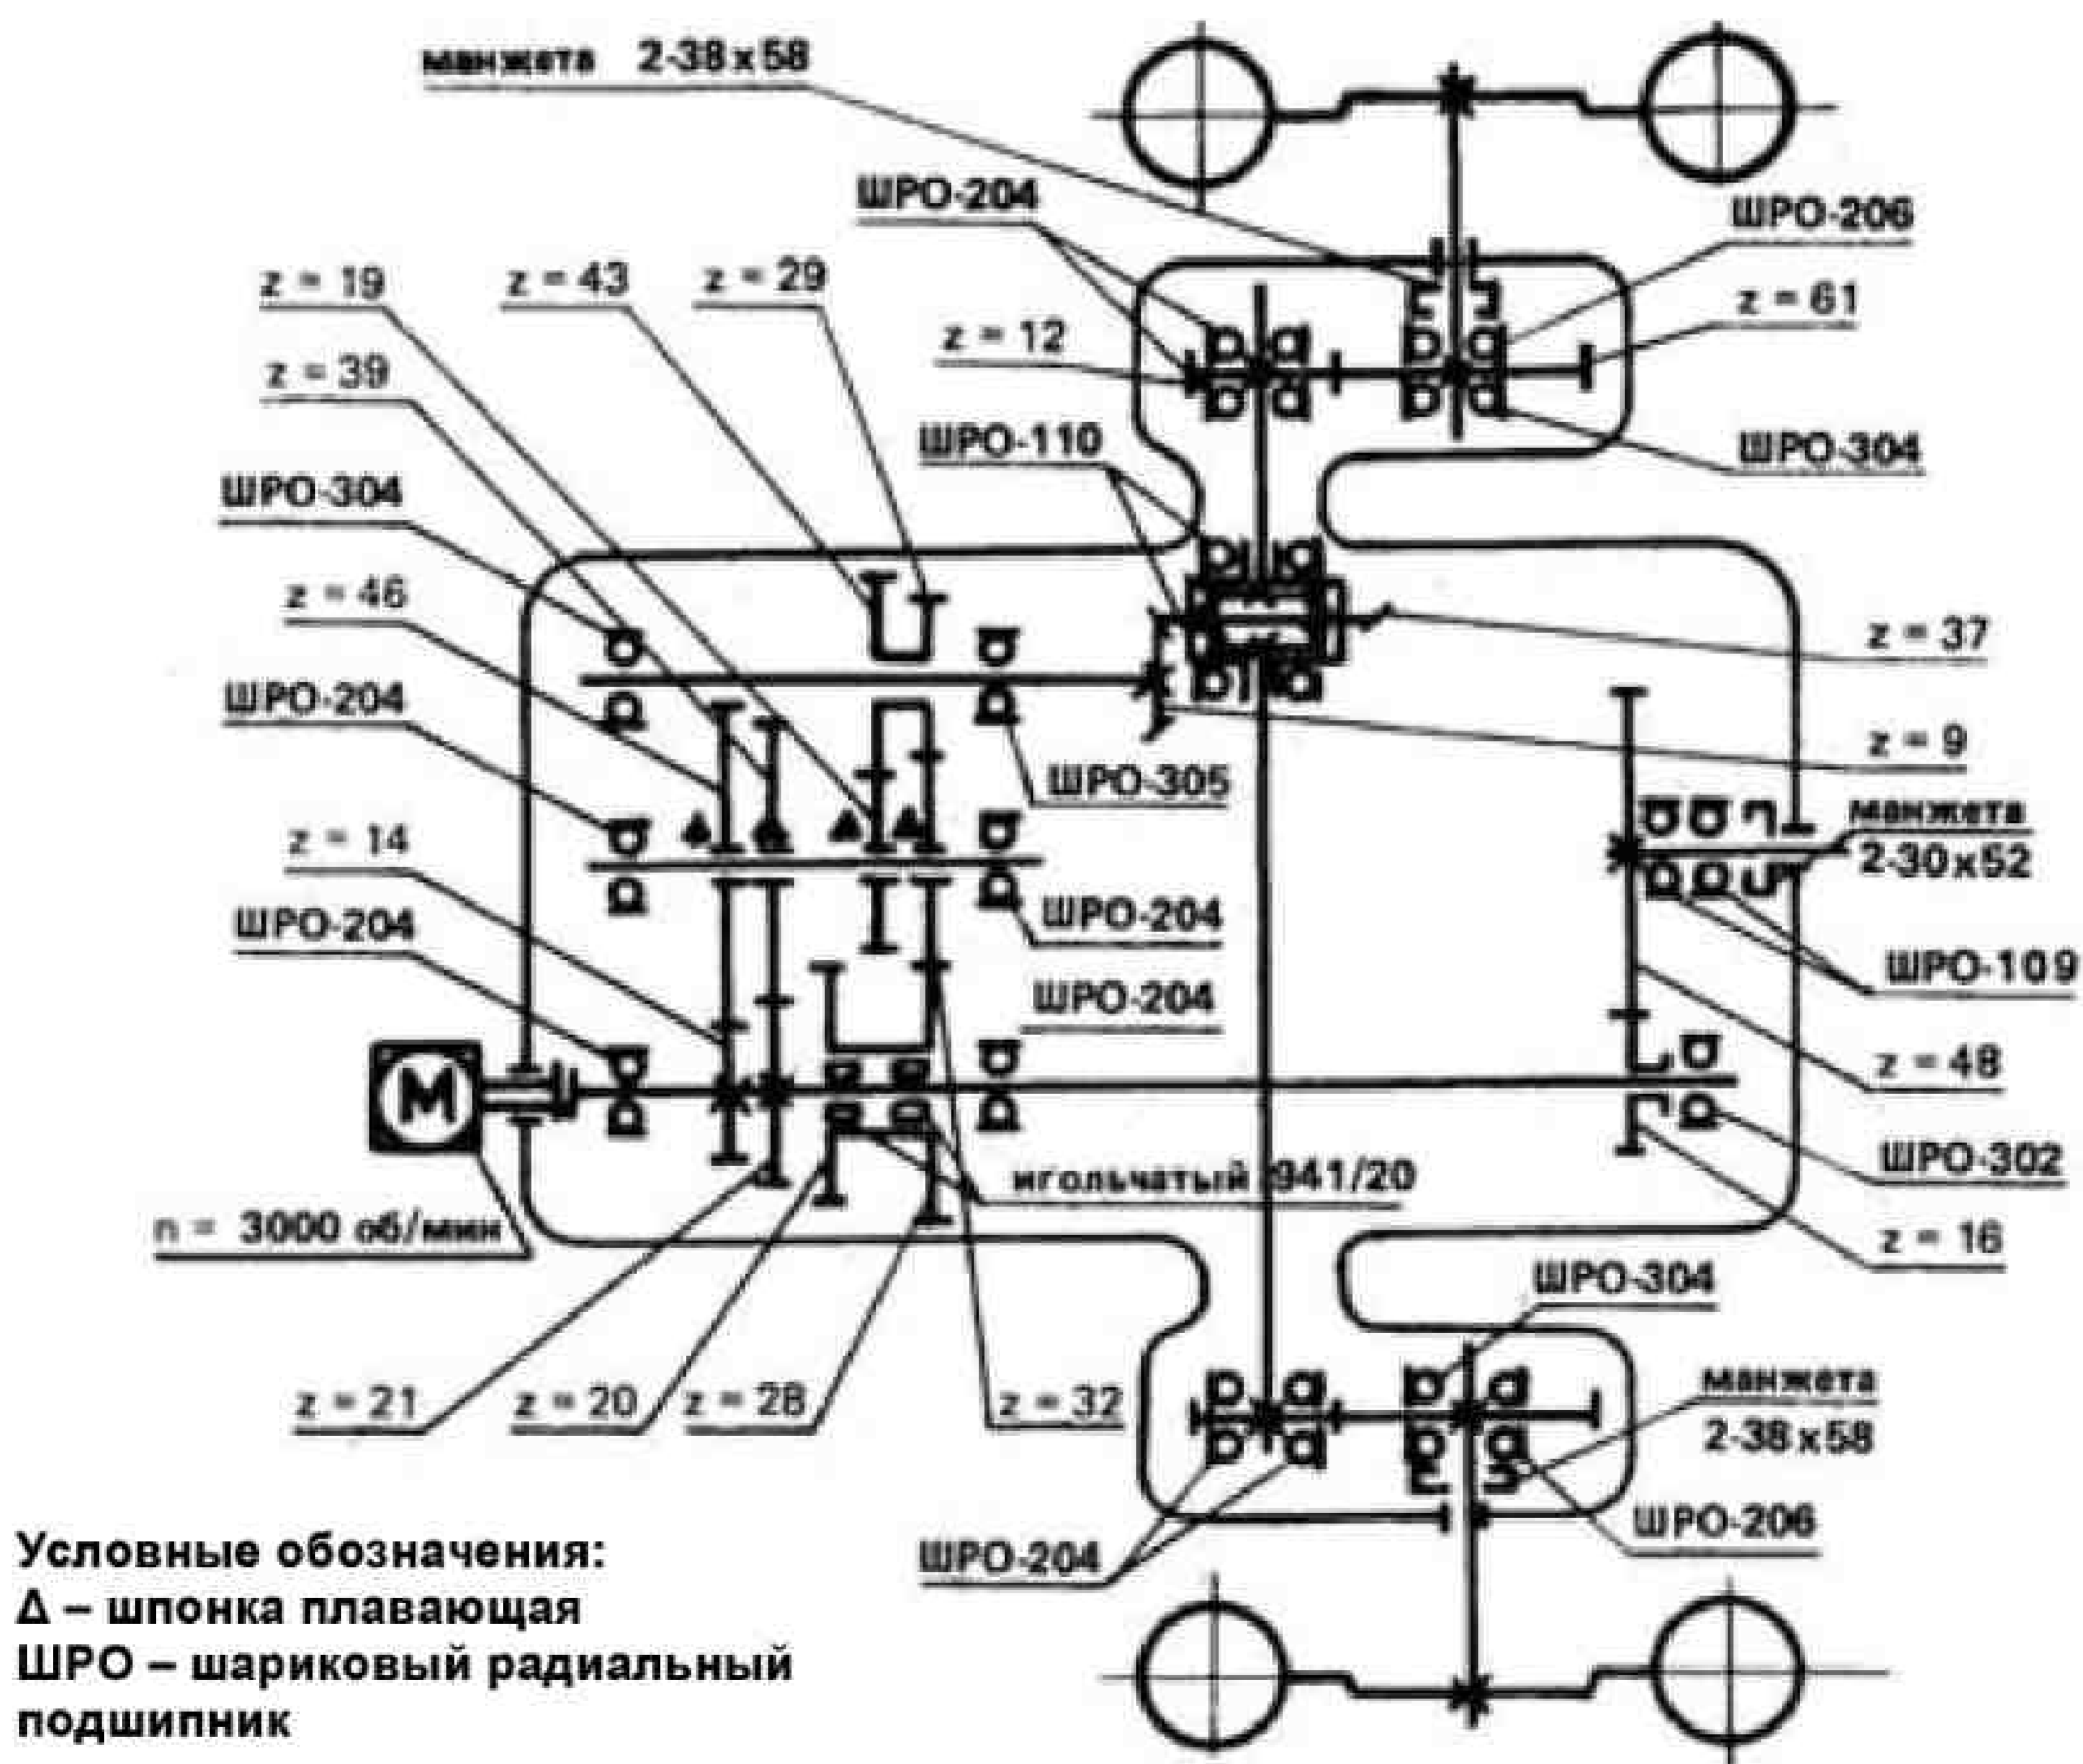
Кинематическая схема силовой передачи мотоблока
